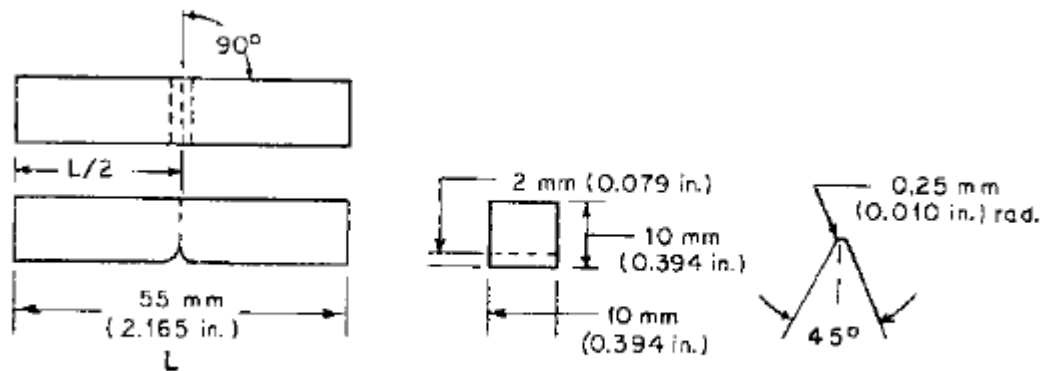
Montage et dimension de l'éprouvette de résilience selon ASTM A370
